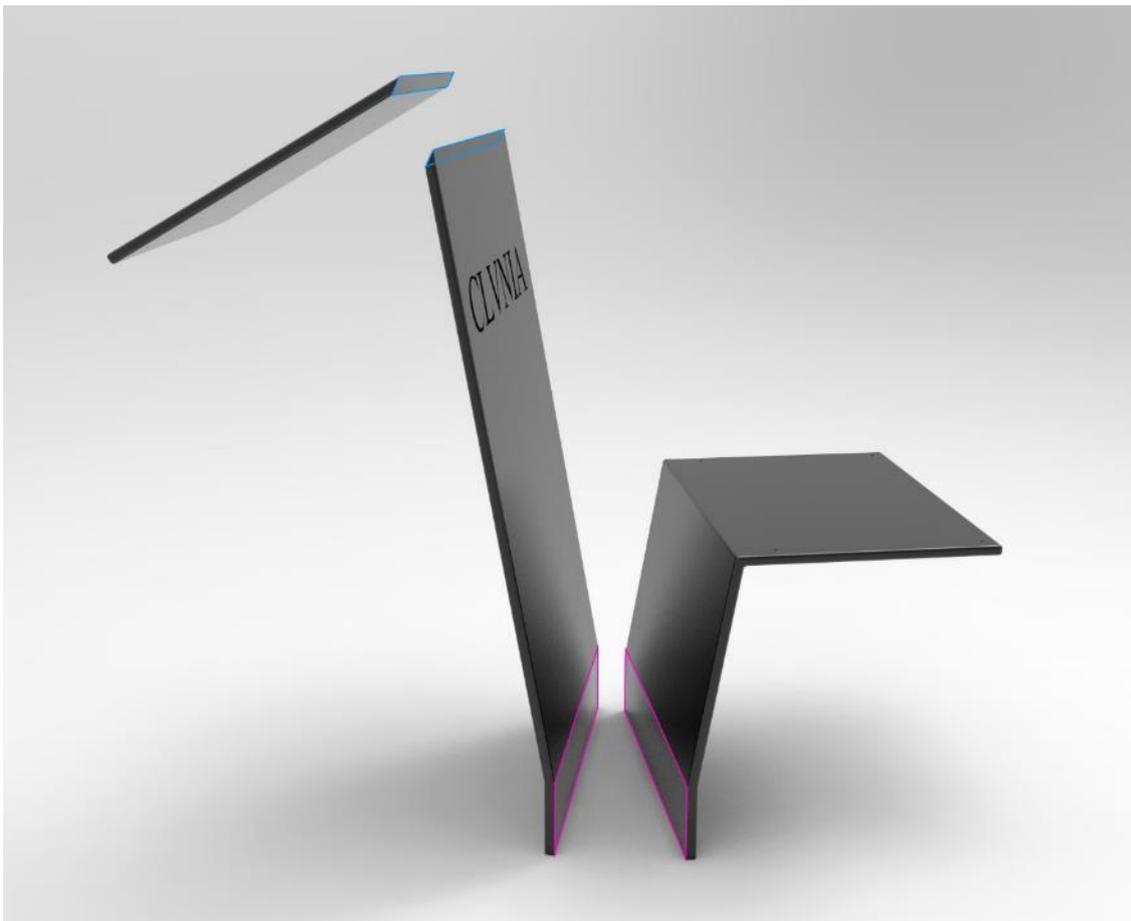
Perímetro de soldadura del conjunto
